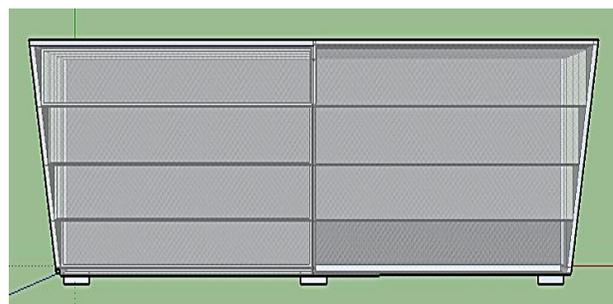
Estructura del DS en 3D, proyección de planta texturizado.
